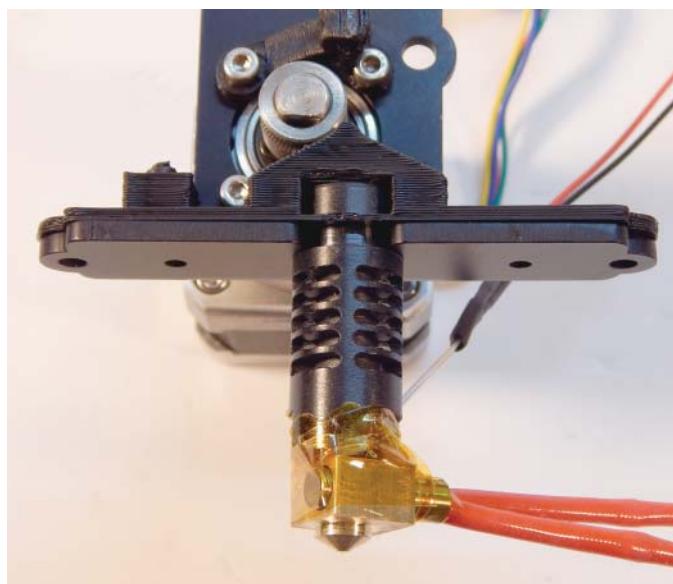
Unser verdrahtetes Hot-End, am Motor und an der Antriebsbaugruppe montiert. Hier handelt es sich um einen vollständigen Thermoplast-Extruder mit gefrästem Antrieb.
